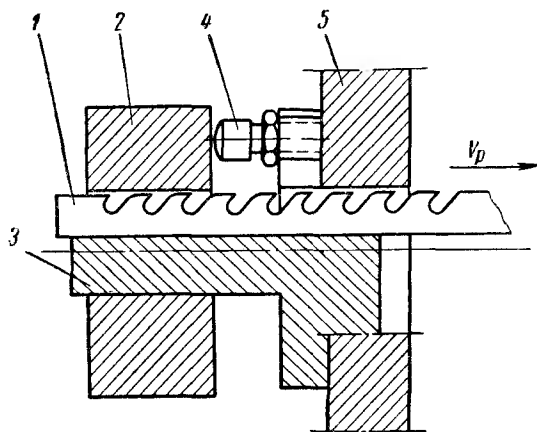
Способ устранения неравномерности глубины шпоночного паза путем установки упорного болта:
